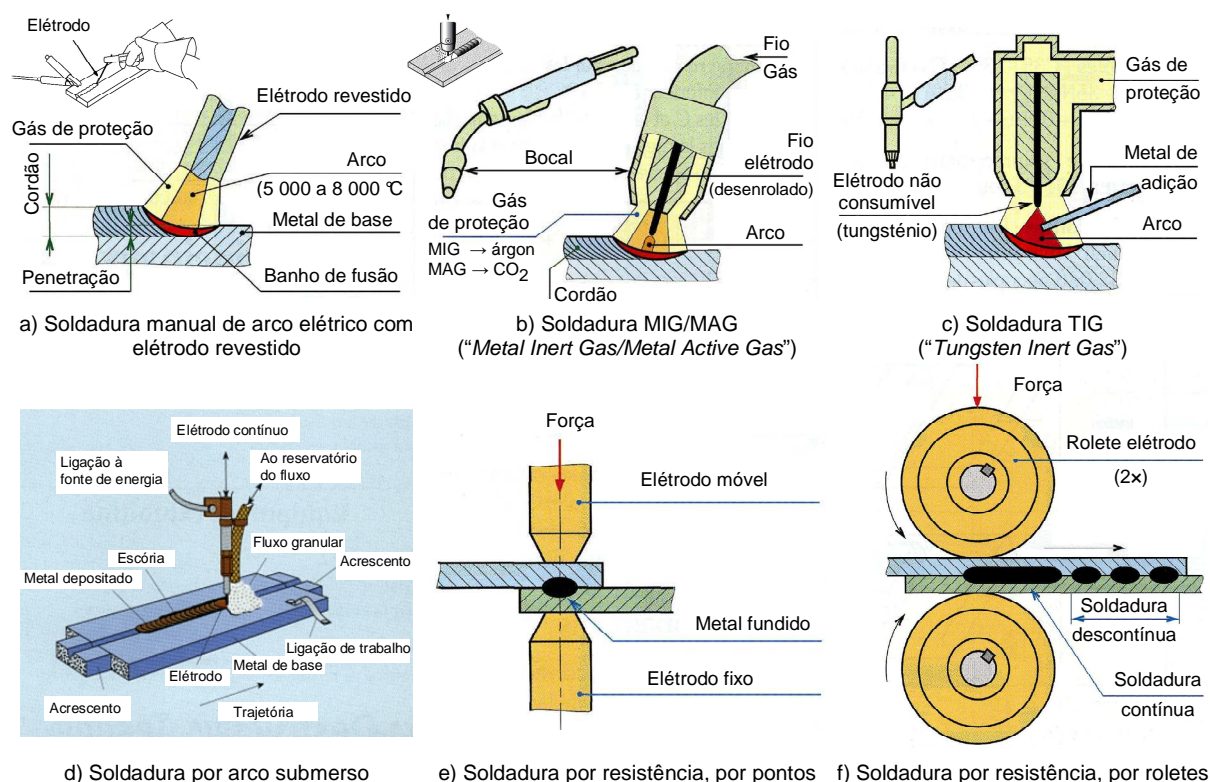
Alguns exemplos de processos de soldadura. Adaptada de [S3]
